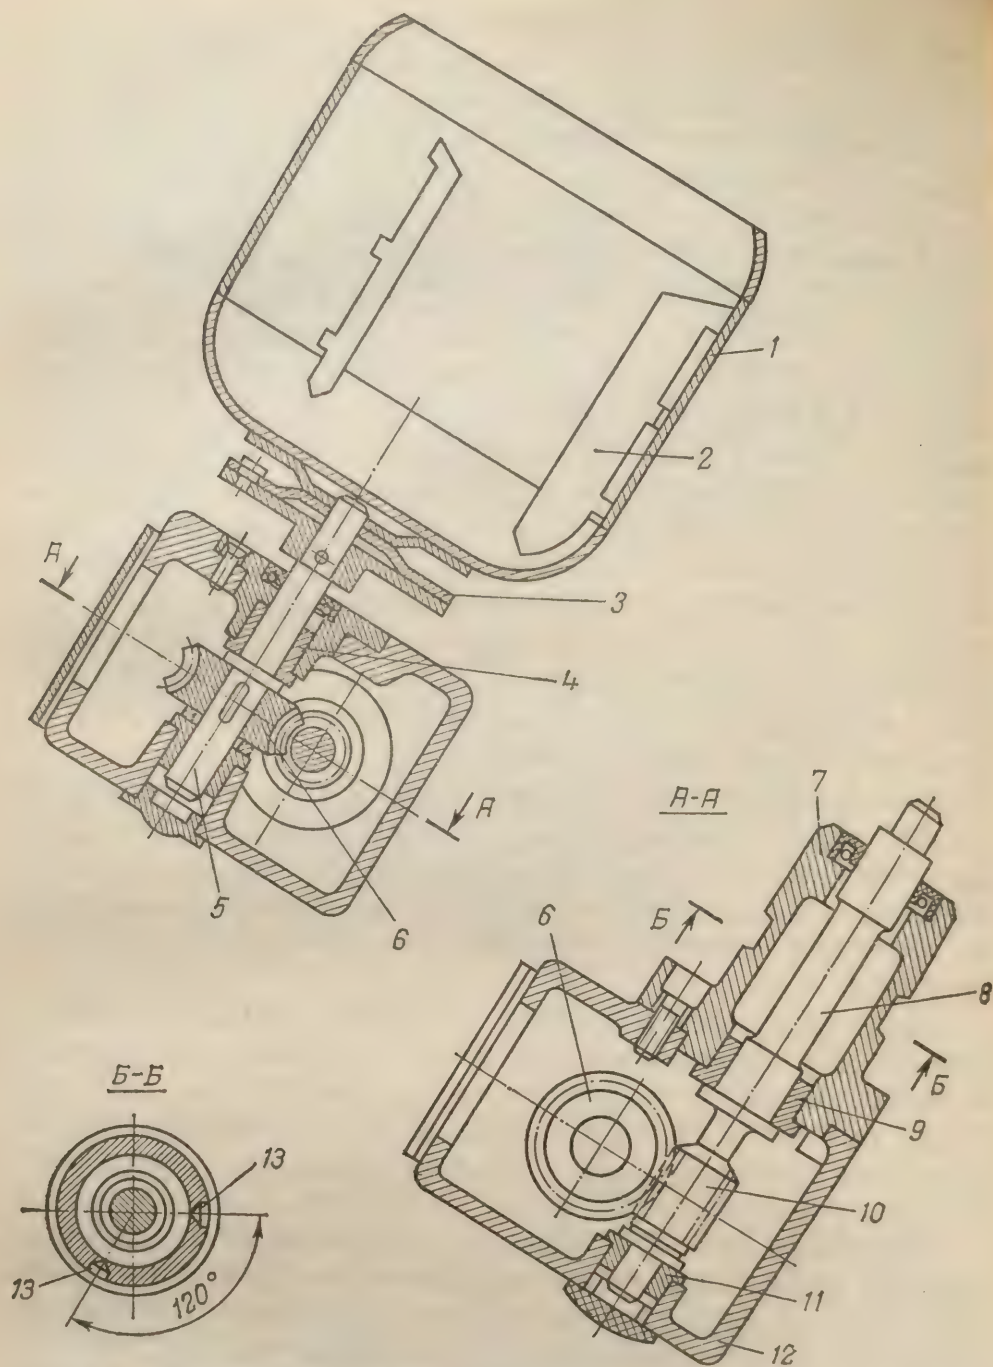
Механизм MC25-200 для перемешивания овощей при приготовлении салатов и винегретов
